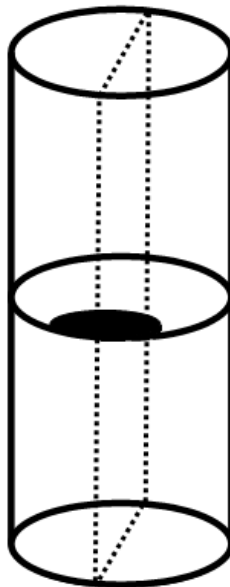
Geometría de referencia: probeta cilíndrica fisurada.
